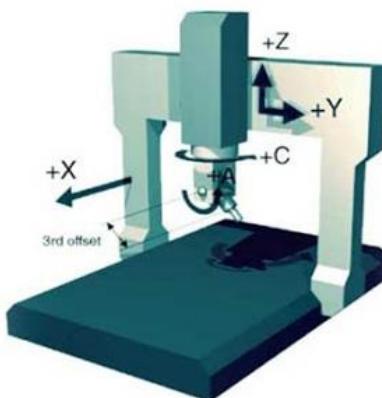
6 Persumbuan Pada Mesin milling 4 Axis
